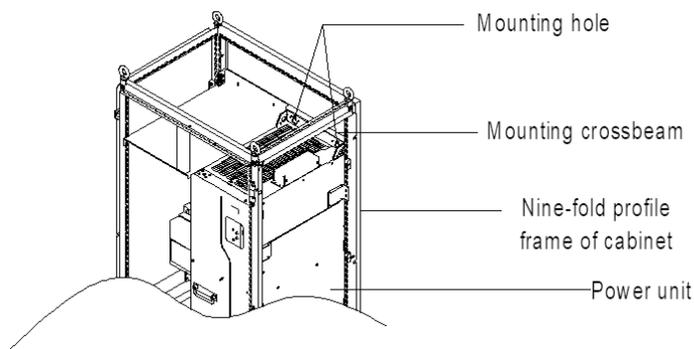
Трехмерный вид крепления EFIP270-280-4-EFIP270-500-4 в шкафу
